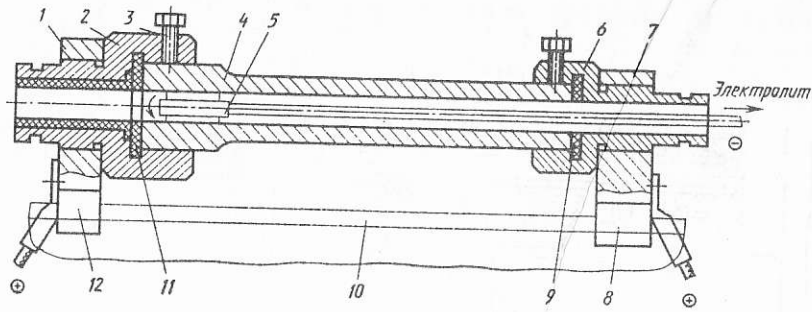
Приспособление для ЭХО отверстий в заготовке с предварительно установленными базовыми элементами
